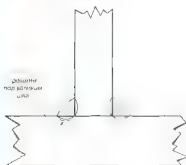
Типичное расположение трещин в сварных швах и под швом
